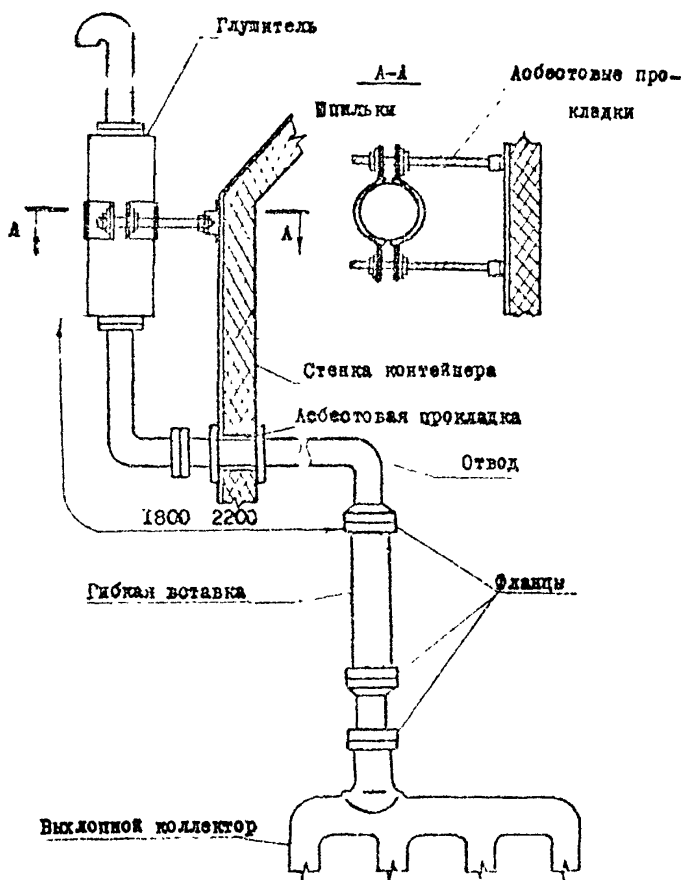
СХЕМА ВЫХОПНОГО ТРУБОПРОВОДА
